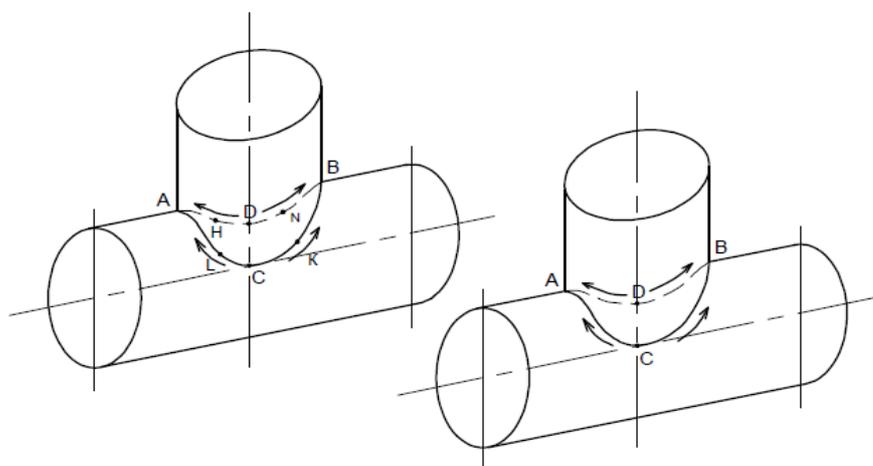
Последовательность сварки углового сварного соединения элементов трубопровода, сварка штуцера
